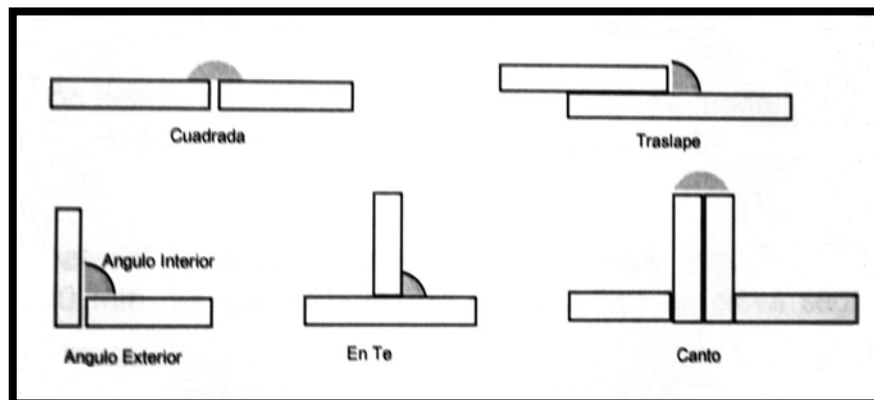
Muestras de las uniones básicas de soldadura MIG
